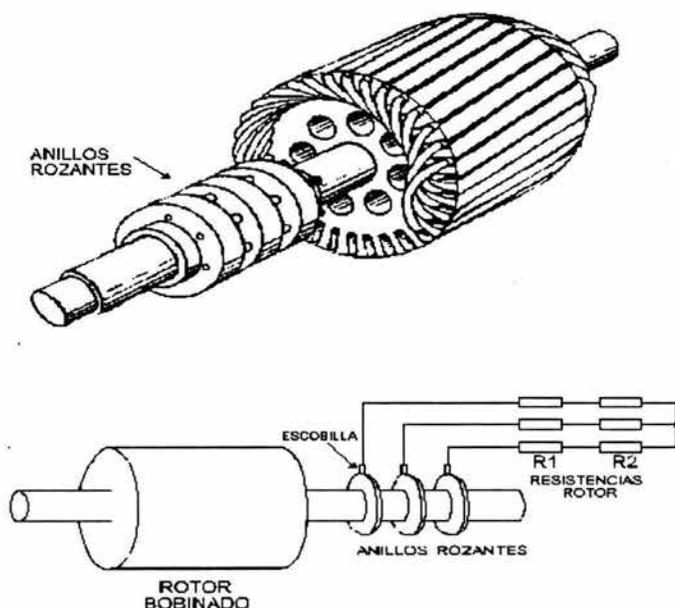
El rotor devanado generalmente se usa en motores de inducción grandes que se operan de una fuente de c-a trifásica.
